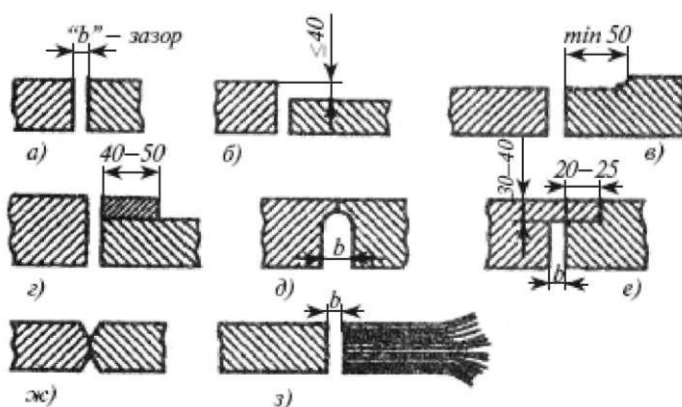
Стыковые сварные соединения: а, б - с равными и разными толщинами свариваемых кромок; в - с уменьшением одной кромки до размеров сопрягаемой; г - с увеличением толщины более тонкой кромки; д - с фигурной разделкой кромок; е - «замковое» соединение; ж - X-образное соединение; з - соединение монолитной кромки с набором пластин
